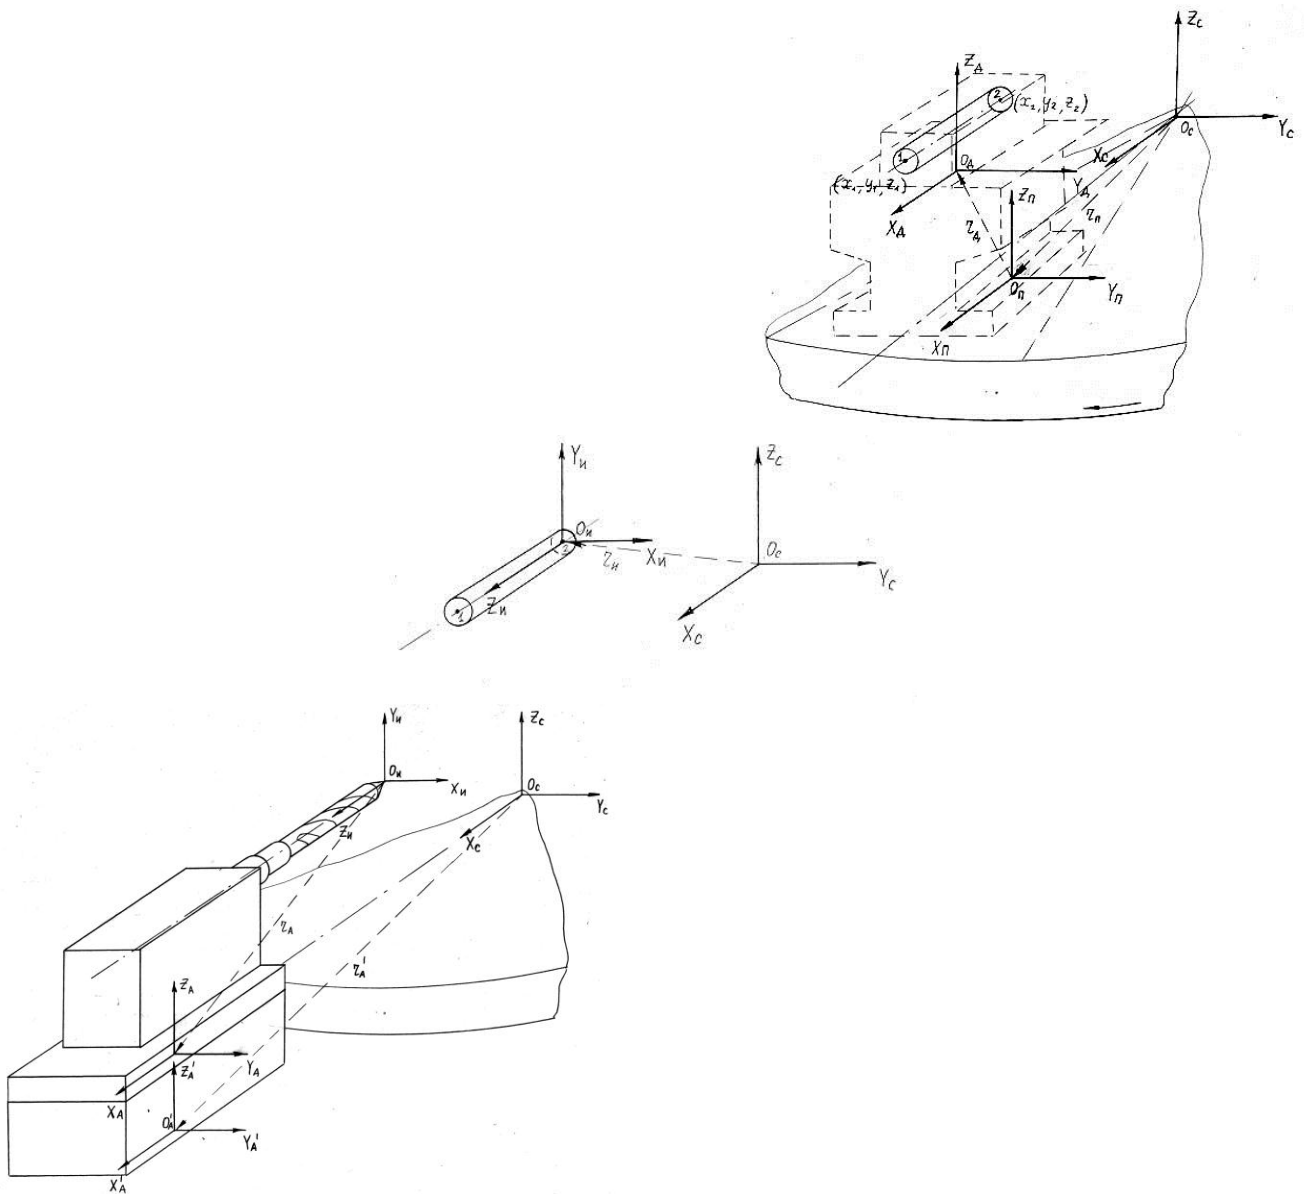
Координатная увязка оснащенного силового агрегата и установочно-зажимного приспособления
